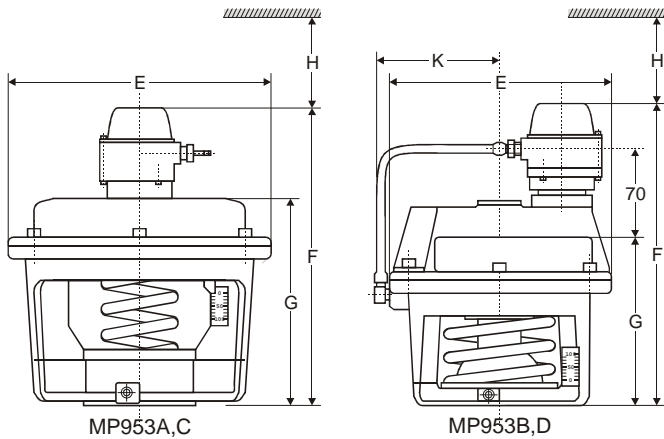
MP953A,C / MP953B,D (dimensions en mm)
